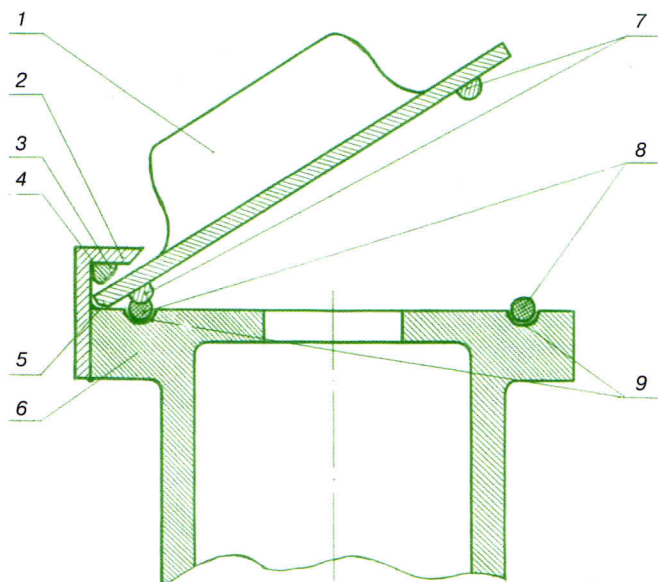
Изменение конструкции крепления крышки блока дизеля над верхним коленчатым валом:
